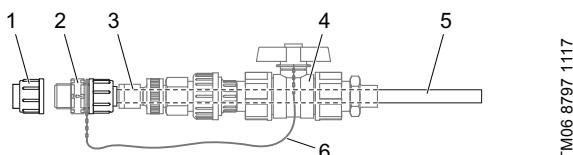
Инжекционный клапан со съёмной впрыскивающей трубой
